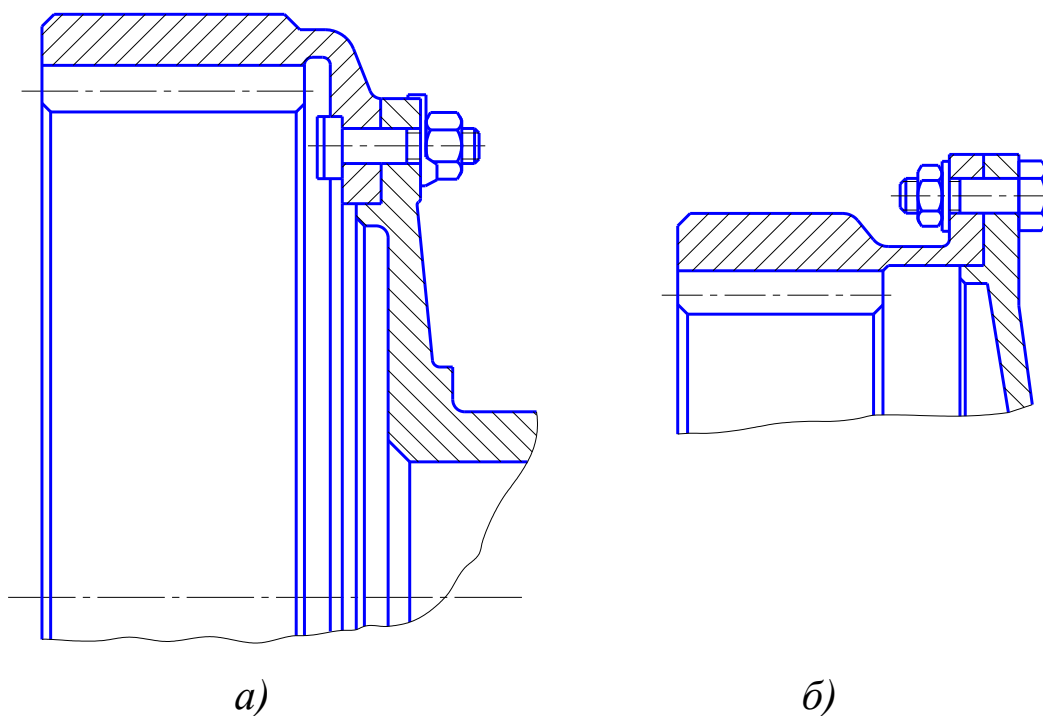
Соединение со ступицей колеса с внутренними зубьями:
